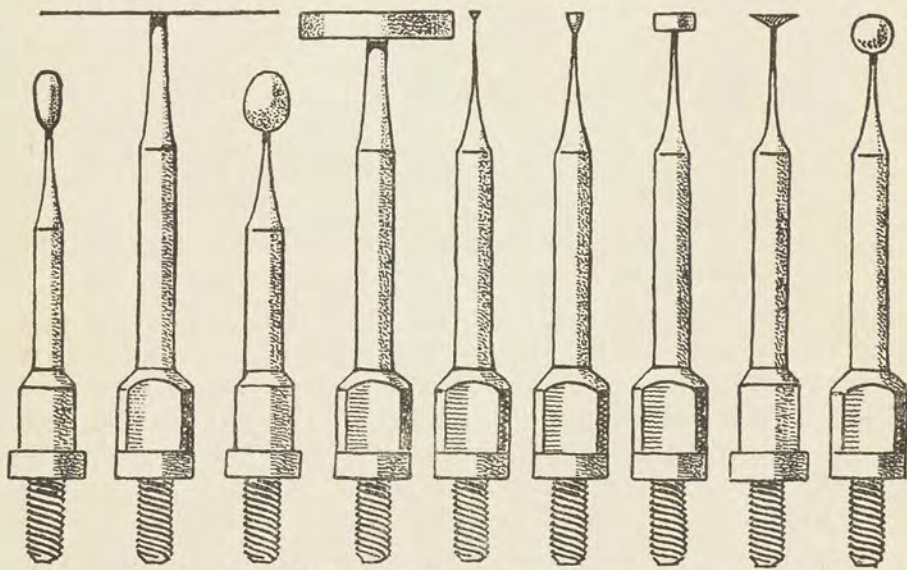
Werkzeuge („Zeiger“) zum Gemmenschneiden.
